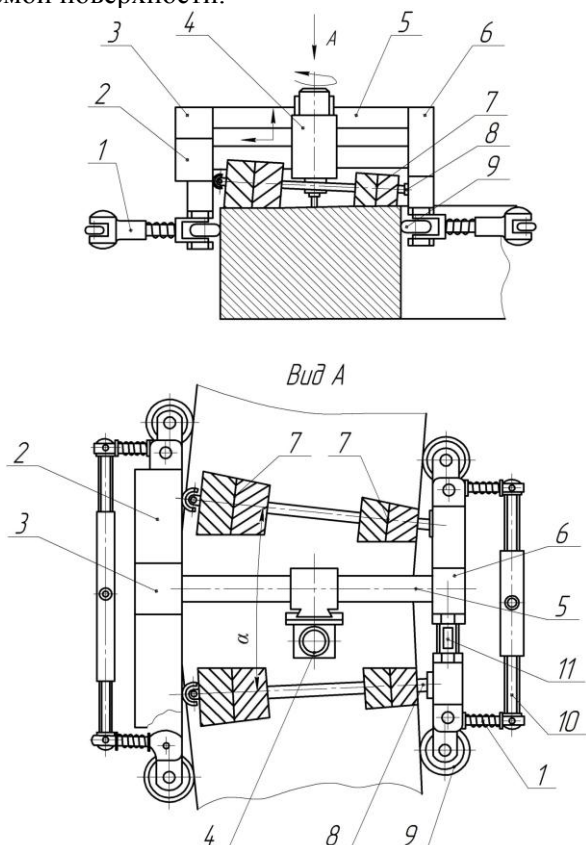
Передвижной фрезерный станок для обработки торцов крупногабаритных деталей
